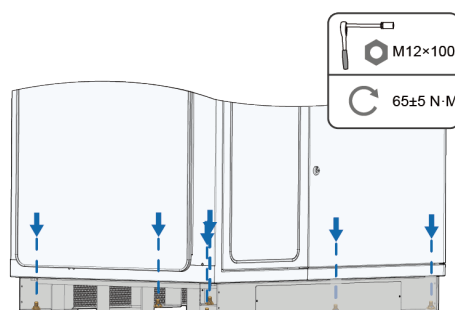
Lage der Bohrungen für Dehnschrauben
